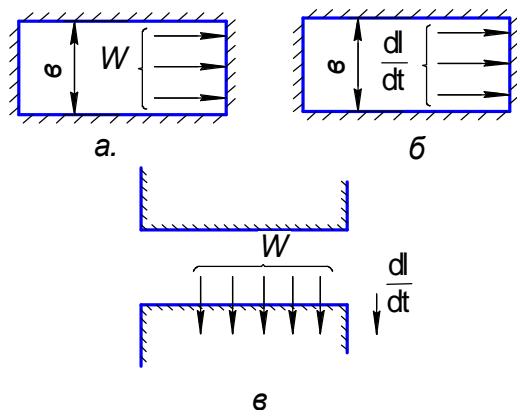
Образование выемки при лазерной резке тонколистовой заготовки
